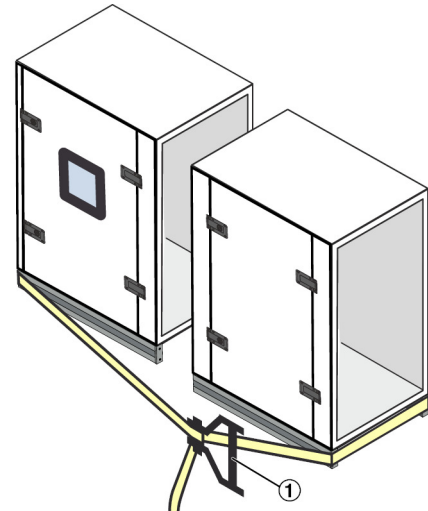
Spanngurt anlegen, mit Grundrahmen
